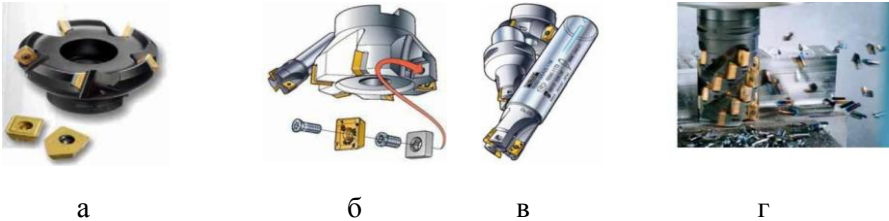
Фрези CoroMill 245 (а); CoroMill 290 (б); CoroMill 390 (в) і двокромочні (г)
